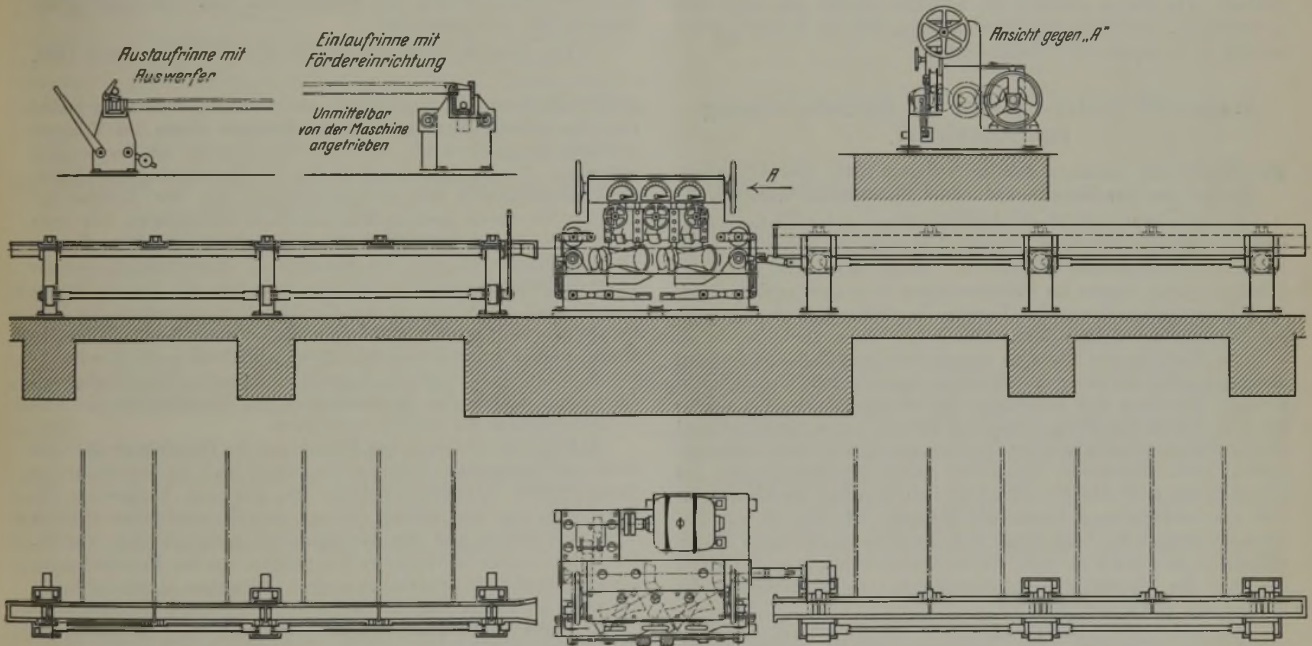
Schrägwalzen-Richtmaschine für Rundstäbe und Rohre.
